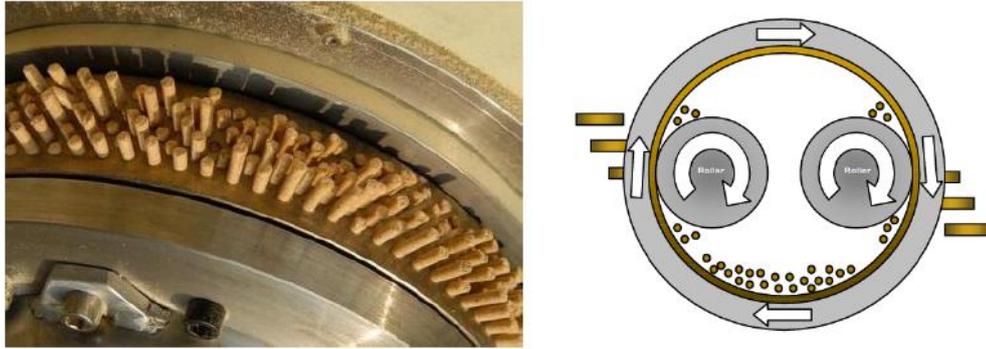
Processo de manufatura de extrusão de pellets (figura adaptada)⁷.
